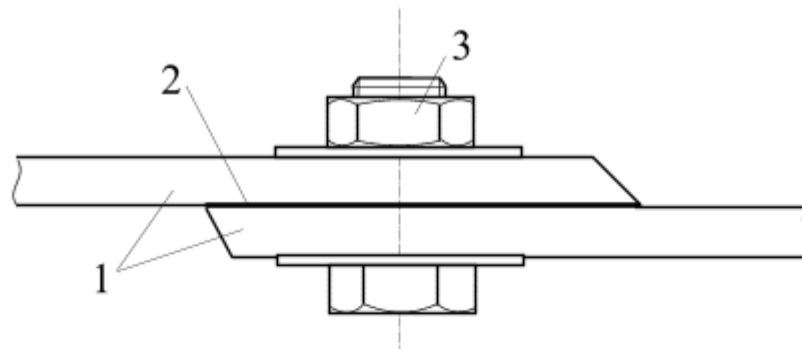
загальний вигляд розбірного контактної вузла
